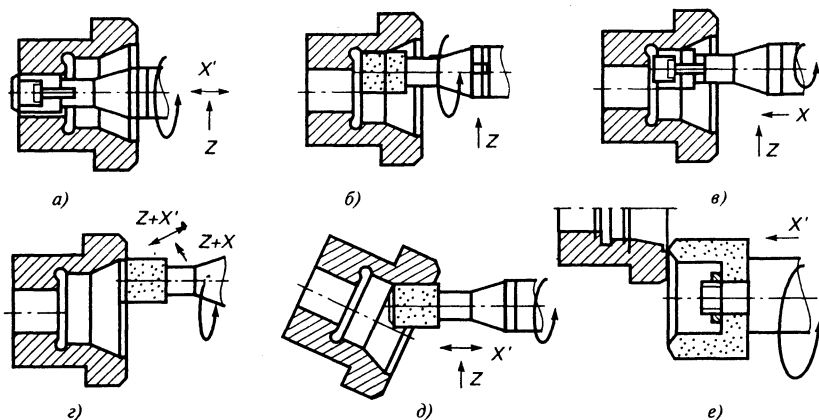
Схема обработки на внутришлифовальном станке с ЧПУ
